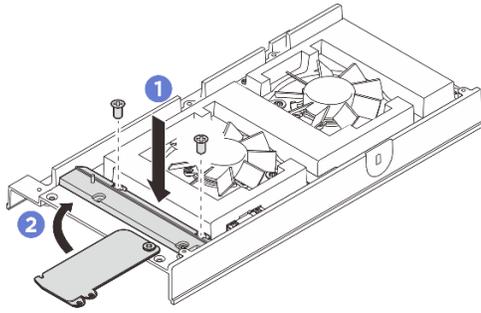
Installazione del coperchio del cavo del bridge della ventola
